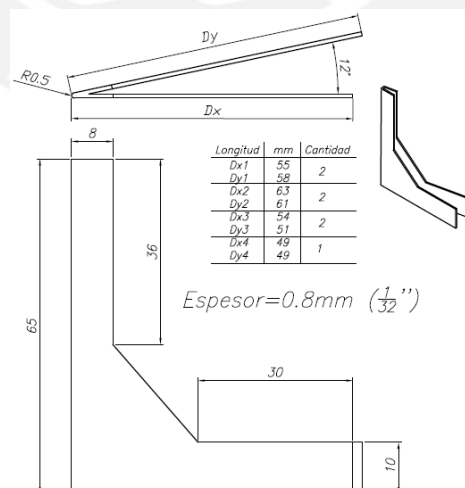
Cuchillas corte tipo Pluma, L1-A4.
